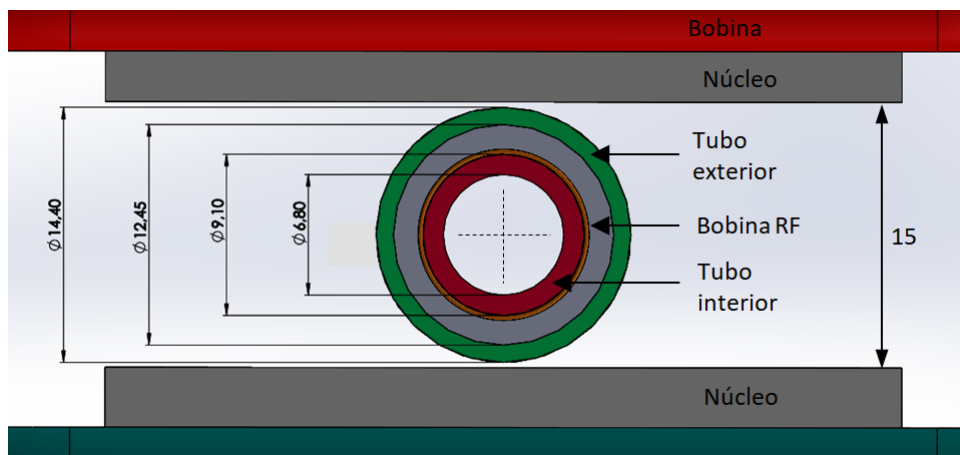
Pormenor do entreferro em corte com o Dewar (mm).
